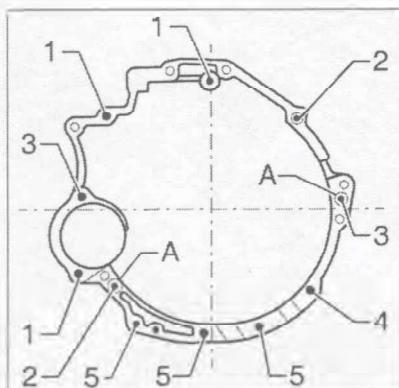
Последовательность затяжки болтов крепления коробки передач (автомобили с 4-цилиндровыми двигателями).
